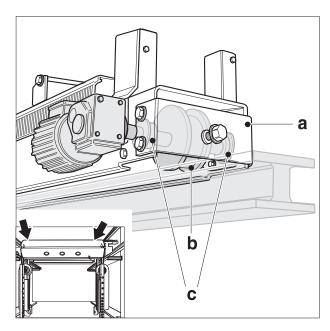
Cuscinetto carrello a carrello b rullo di guida c cuscinetto rullo di guida
